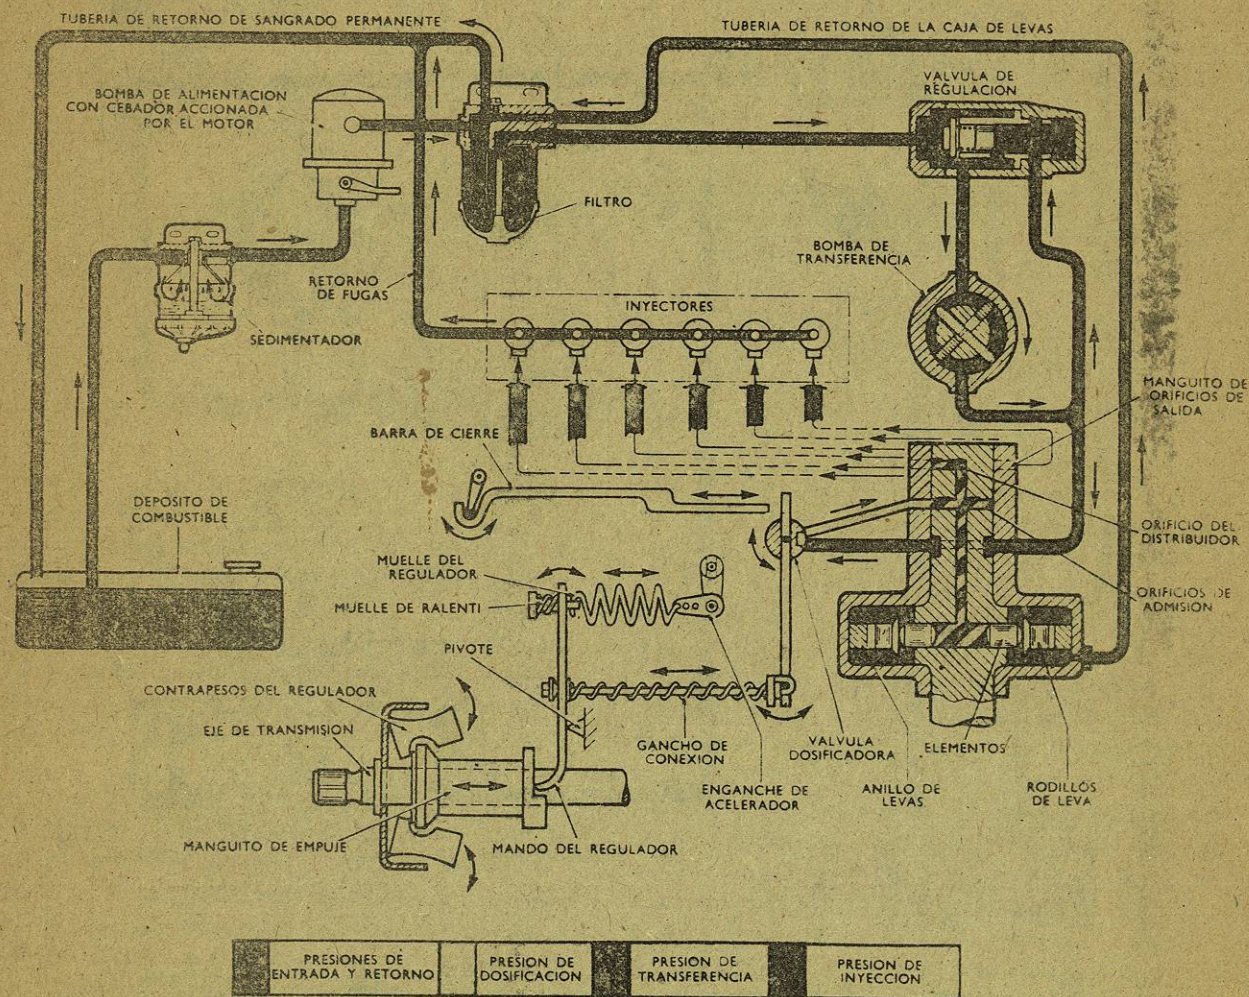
Sistema de combustible de una bomba DPA y regulador mecánico
